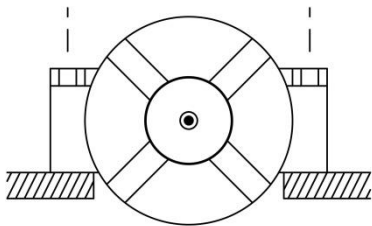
Montaje del alternador, montaje en almohadilla, vista superior
